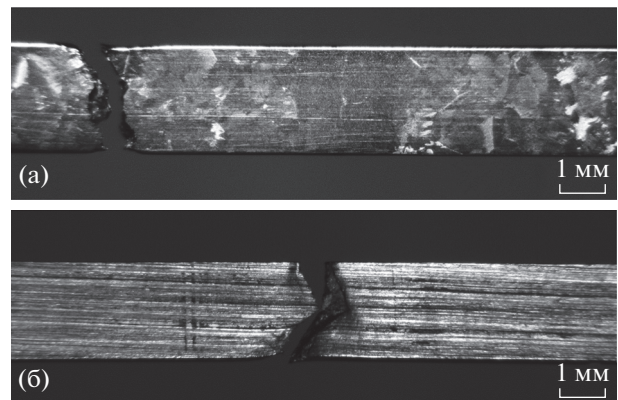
Вид боковой поверхности рабочей части необработанных (а) и после УЗОТ (б) разрушенных образцов со сварным соединением напечатанного сплава Ti–6Al–4V в результате циклических испытаний на растяжение.
